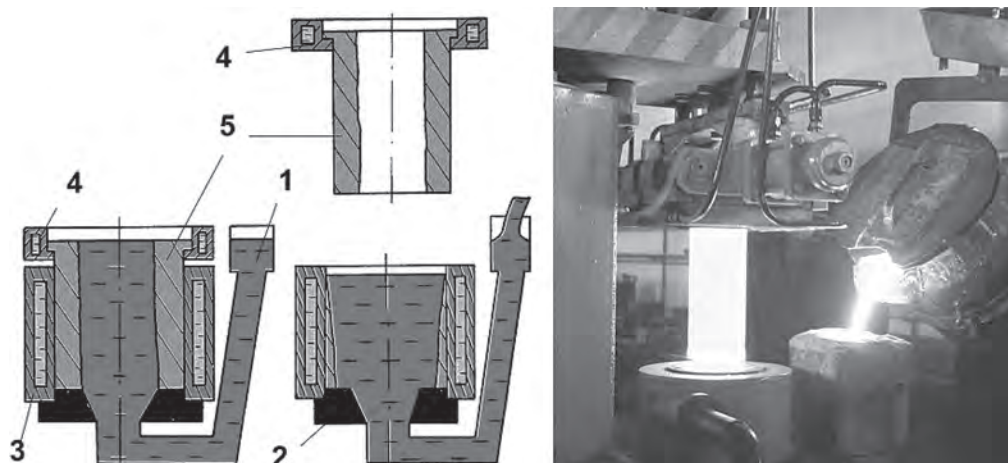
Принципиальная схема и процесс непрерывно-циклического литья полых заготовок без стержня: 1 – металлопровод; 2 – соединительный стакан; 3 – стационарная часть кристаллизатора; 4 – подвижная часть кристаллизатора (захваты); 5 – отливка
